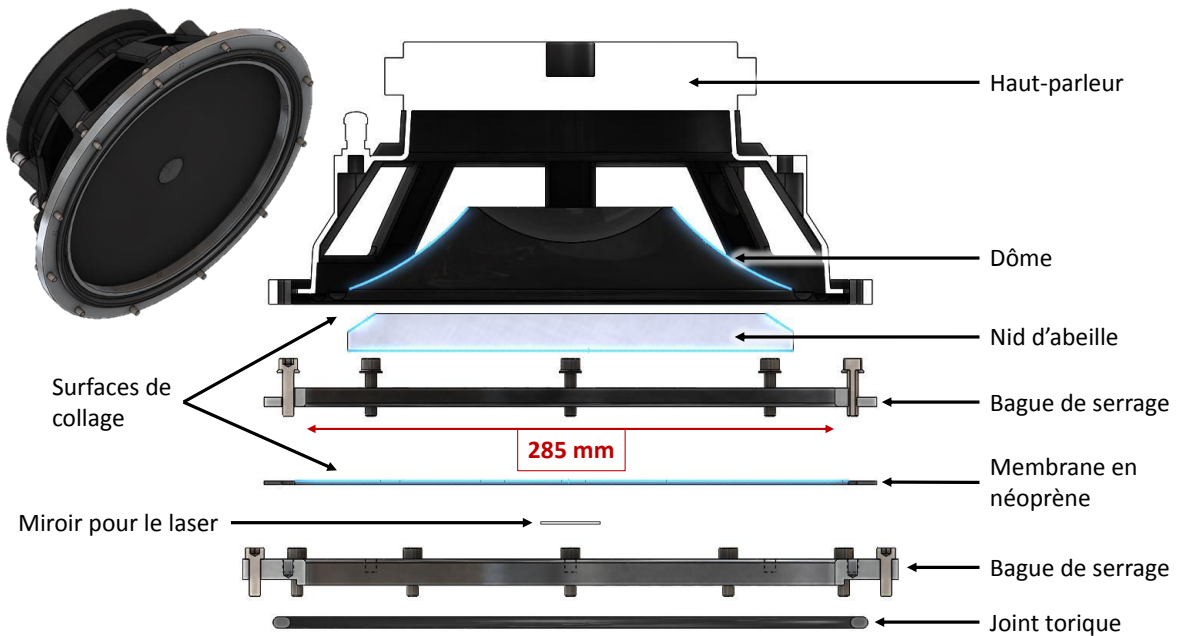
Détails sur le piston : un haut-parleur accessoirisé.
